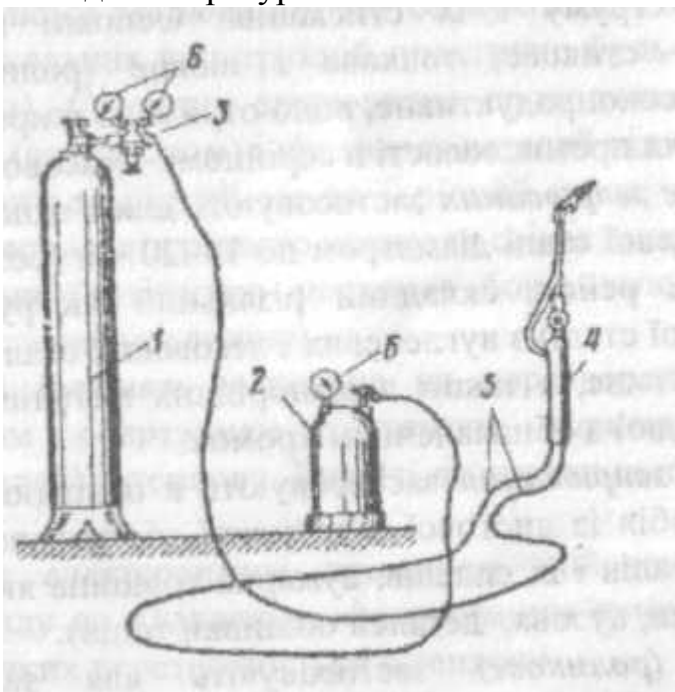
Гасокиснева установка для різання металів: 1 - кисневий балон; 2 - бачок з гасом; 3 - редуктор; 4 - гасовий різак; 5 - гумові рукави; 6 - манометри
